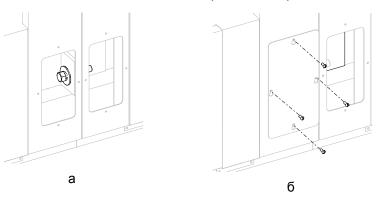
Внешний вид узла соединения без крышки (а) и с
